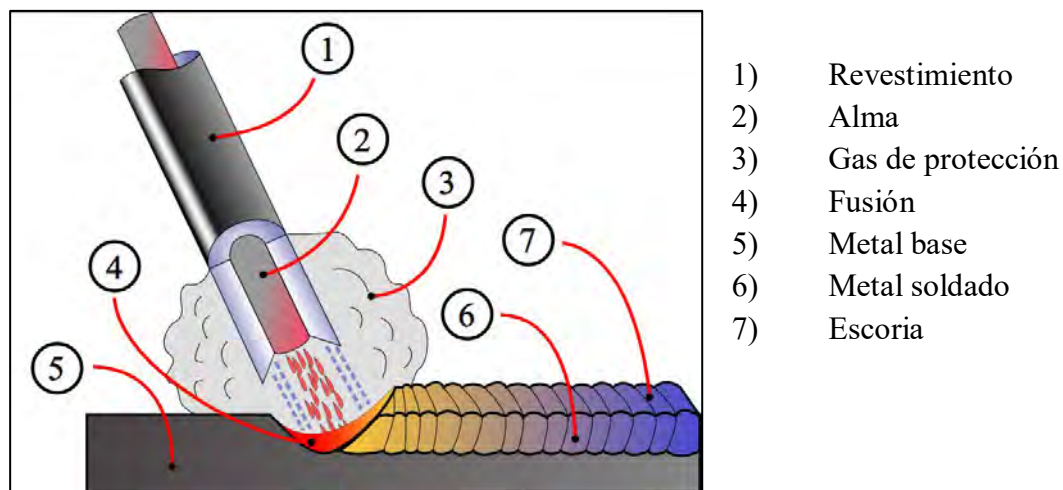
Esquema simple de proceso de soldadura SMAW
